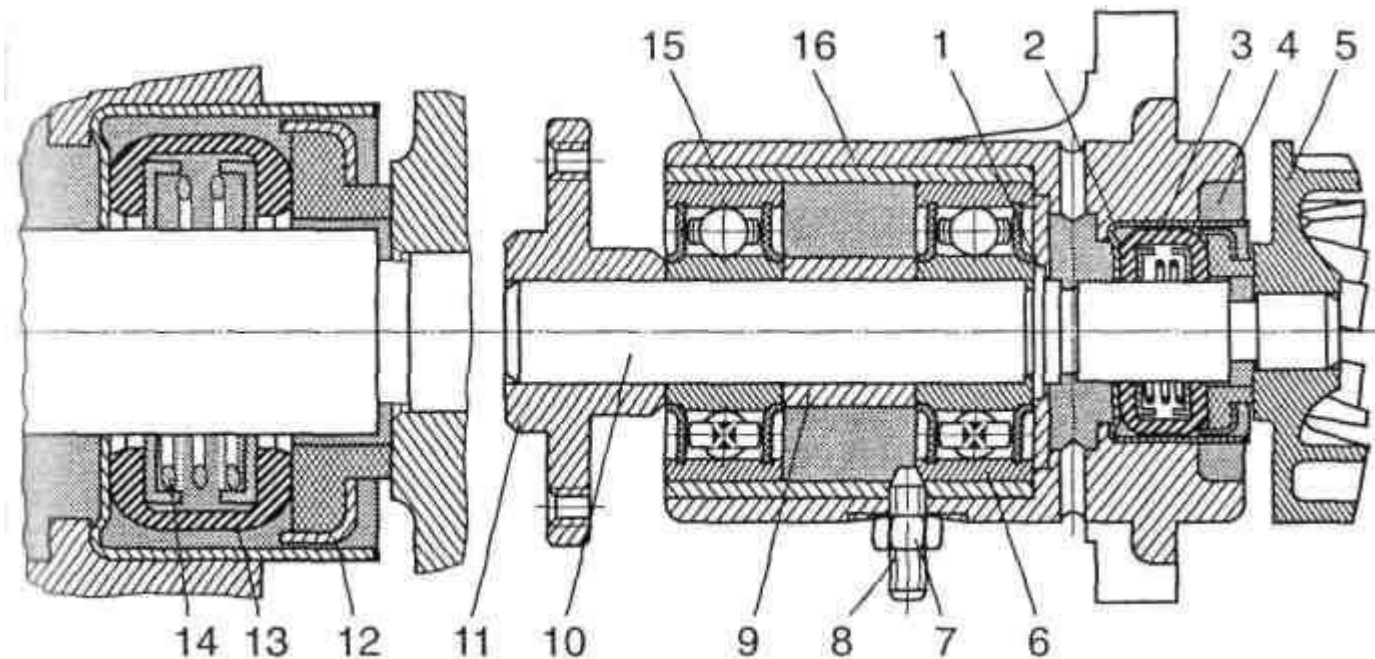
Водяний насос: 1 - стопорне кільце; 2 - корпус ущільнювача; 3 - манжета; 4 - ущільнювальна шайба; 5 - крильчатка; 6 - підшипник; 7 - контргайка; 8 - стопорний гвинт підшипника; 9 - розпірна втулка; 10 - вал; 11 - маточина; 12 - корпус ущільнювальної шайби; 13 - обойма; 14 - пружина; 15 - стакан підшипників; 16 - корпус насоса
